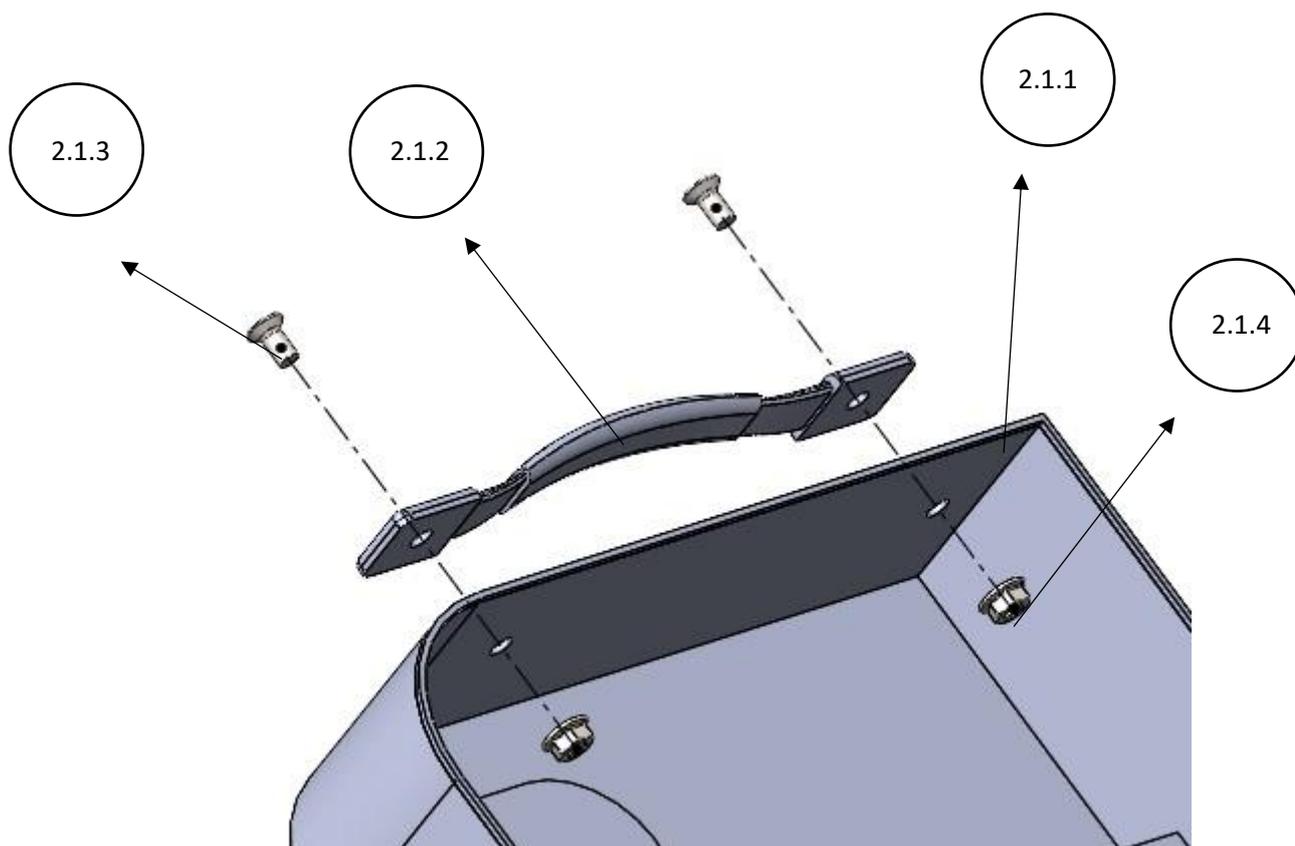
Ensamblaje rediseño final del subconjunto 1
